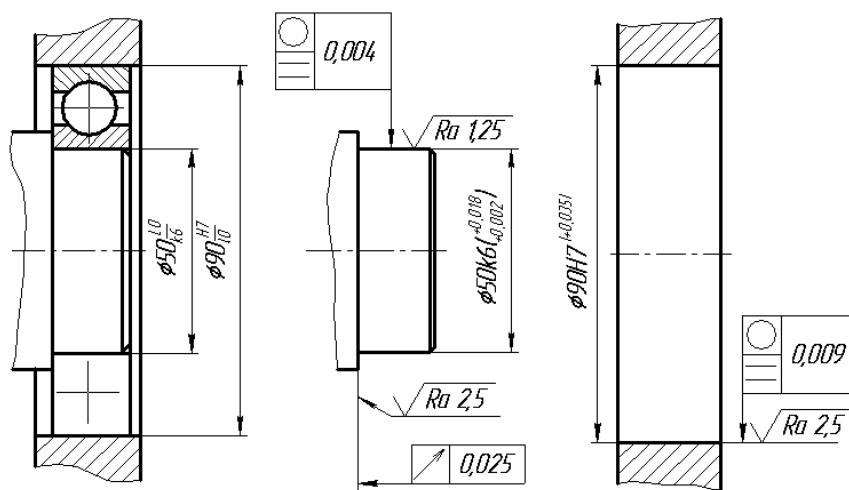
Эскиз подшипникового узла, вала и корпуса
